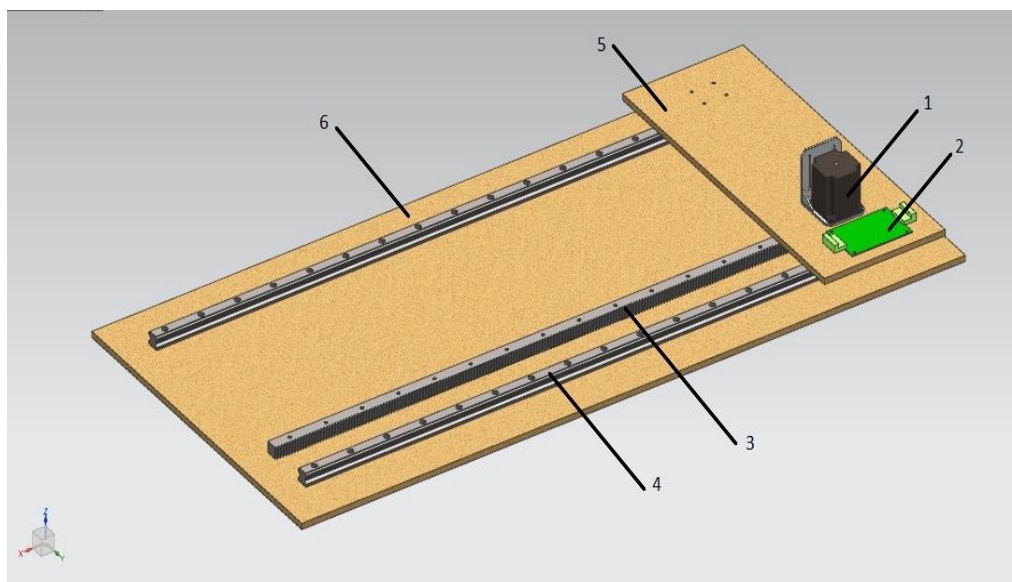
Система линейного перемещения робота-манипулятора: 1 – Шаговый двигатель NEMA 23 (ST57-56); 2 – Драйвер шагового двигателя ST57-1; 3 – Зубчатая рейка M 1,5; 4 – Продольный рельс; 5 – Площадка манипулятора; 6 – База
